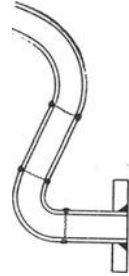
Aus Rohrbogenformstücken zusammengeschweißtes Ausgleichrohr (Lyra-bogen).
